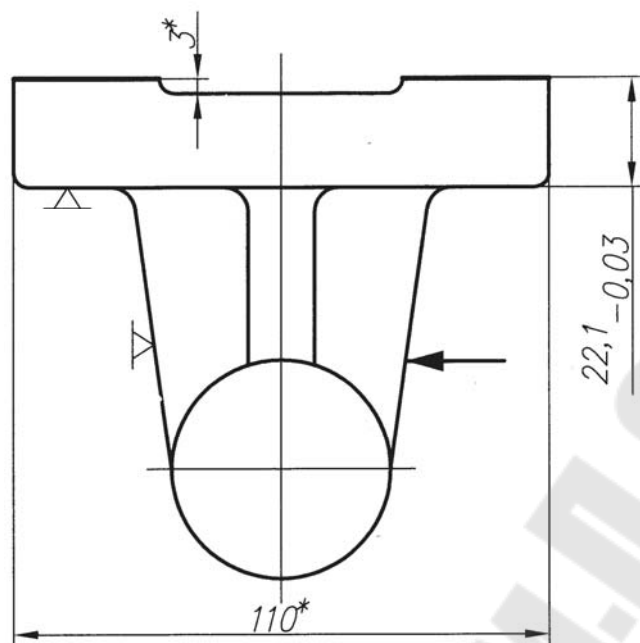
Операционный эскиз фрезерной обработки детали с указанием схемы базирования
